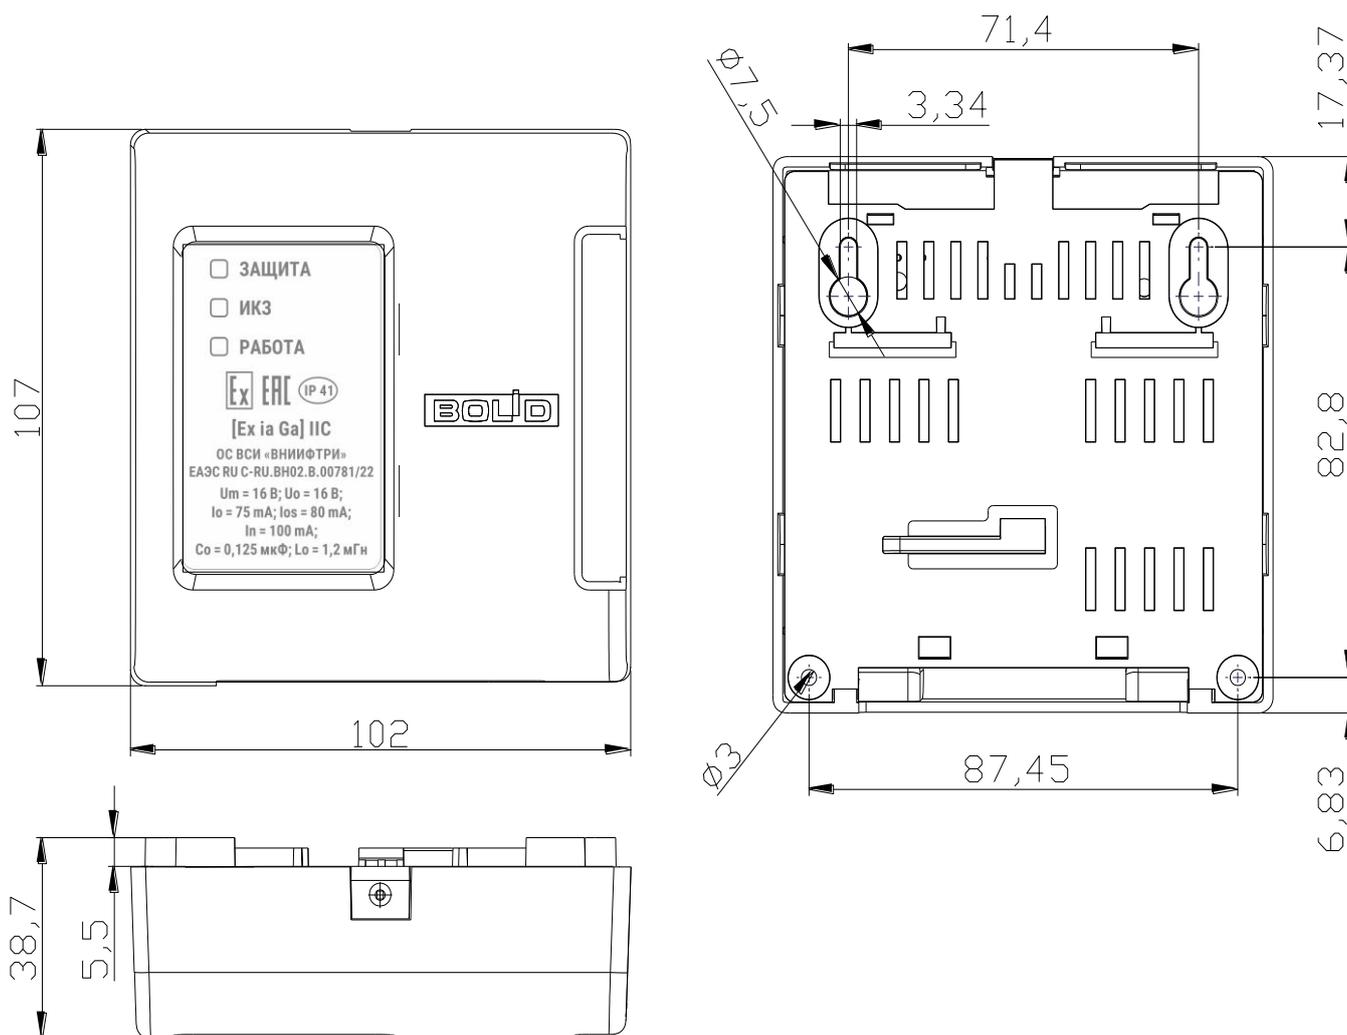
Габаритный чертёж «С2000-Барьер-Exi»
